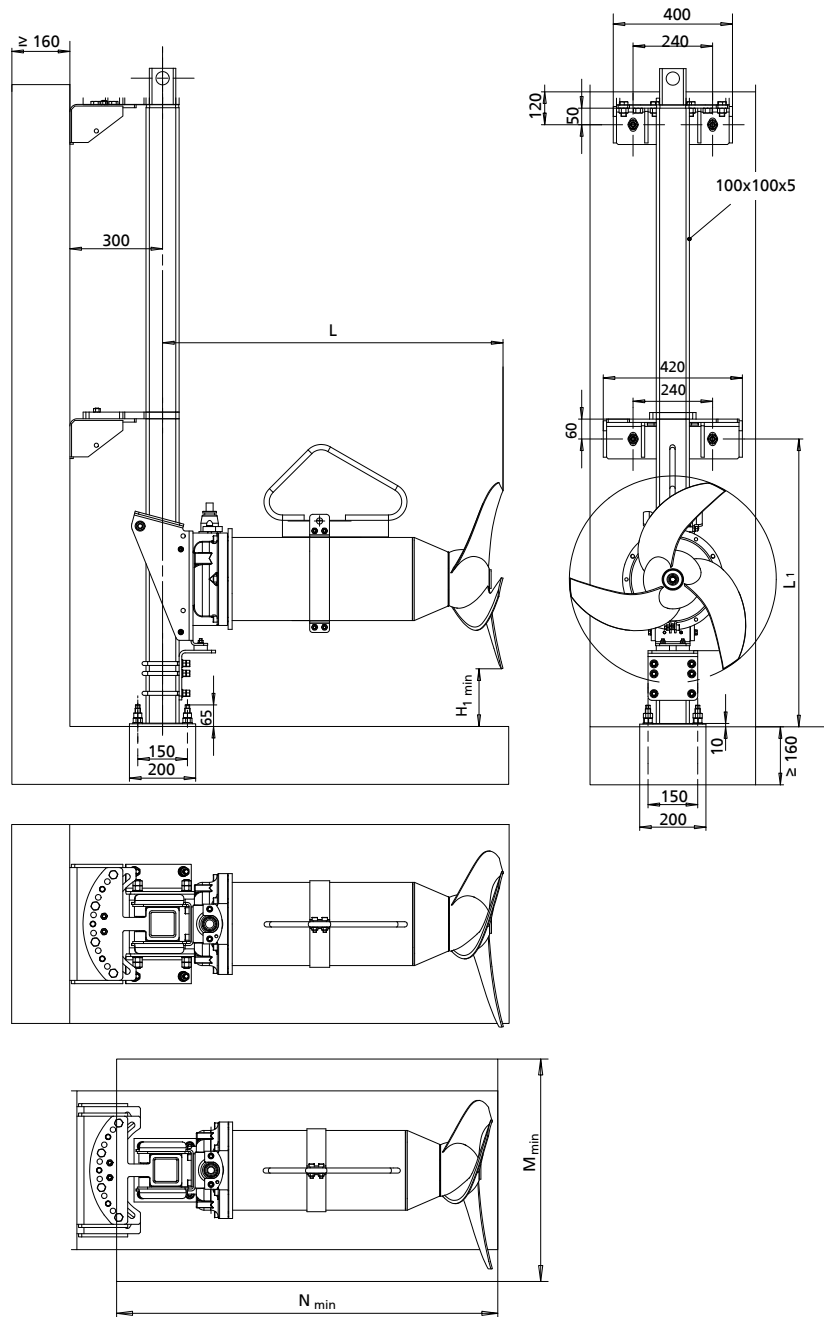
Установка принадлежностей 22 — Атаміх 400 (только типоразмер 4135) / 600
